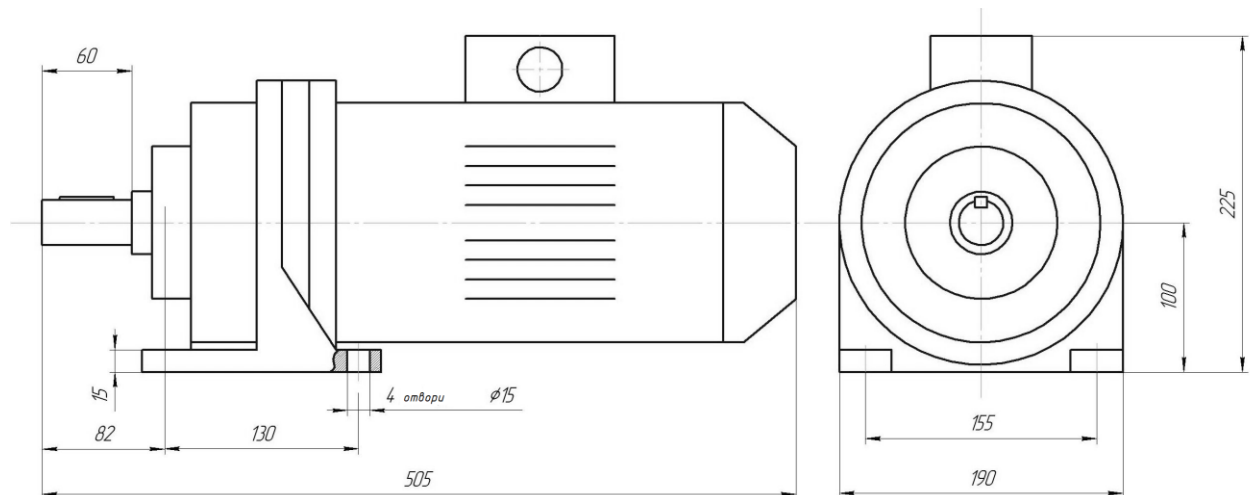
Загальний вигляд мотор-редуктору типу ЗПМ-125
